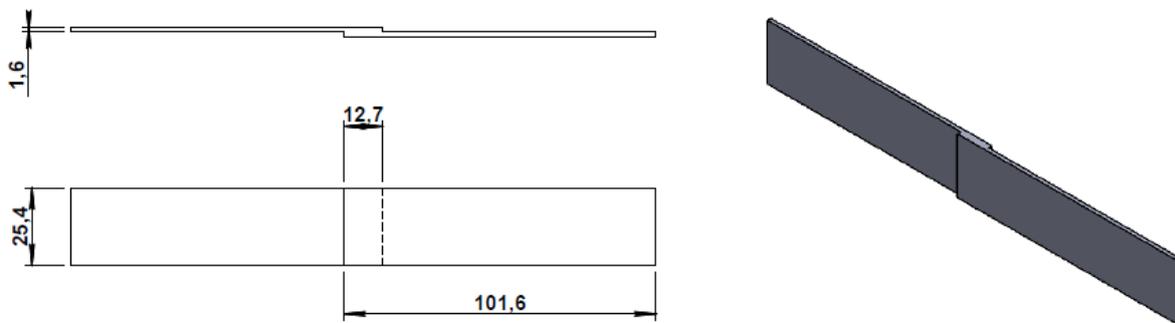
Dimensões e forma das juntas de sobreposição simples em mm.
